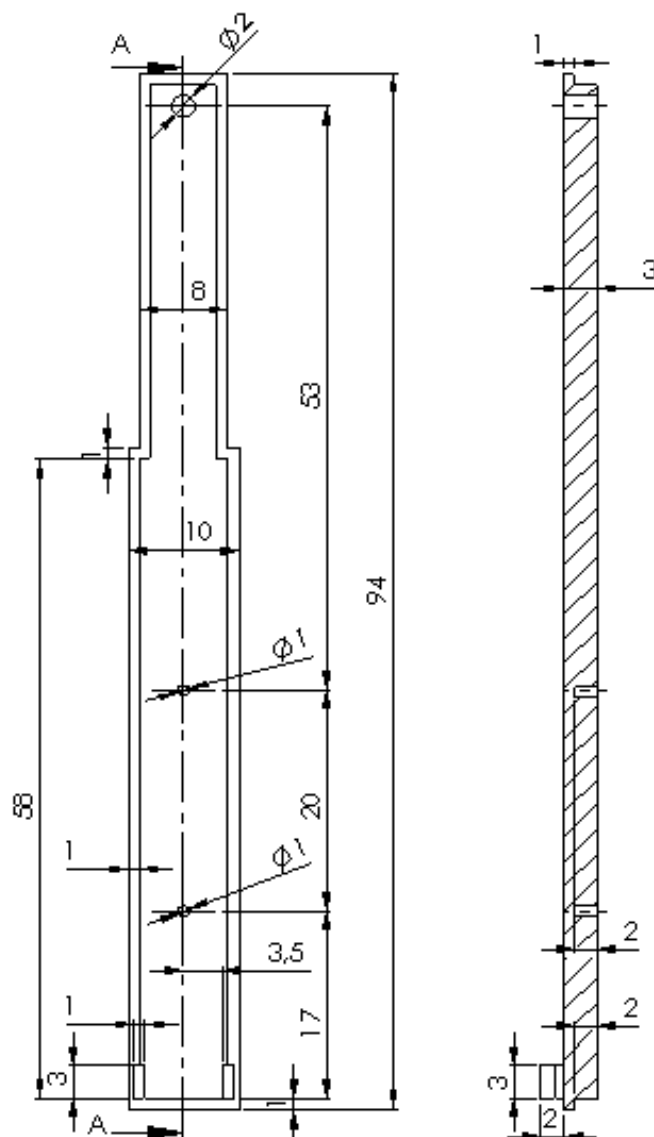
Tapa dels controls electrònics. Vista de planta inferior (a la dreta) i vista de secció A-A de la planta inferior (esquerra).
